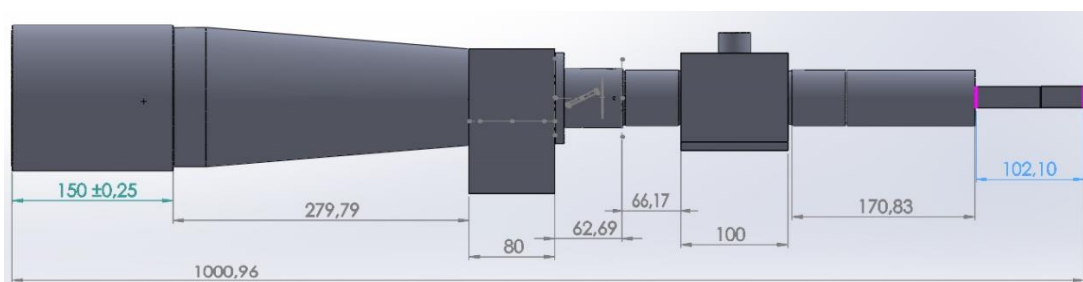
Die konstruierte Sonde mit Bemaßungen in Millimeter.
